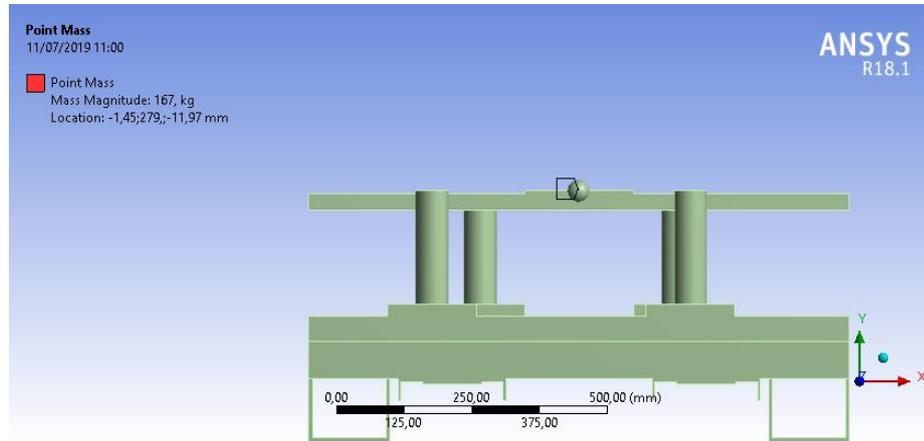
Faces de referência da aplicação do ponto de massa
